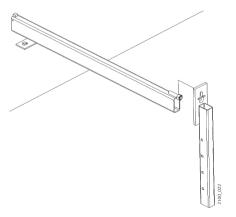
Montage de la fixation à encoches en trou de serrure sur la poutre
